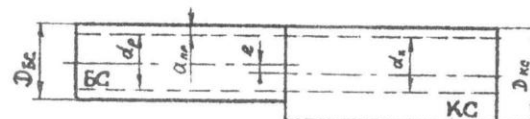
Определение диаметров заготовок инструментов под сварку
